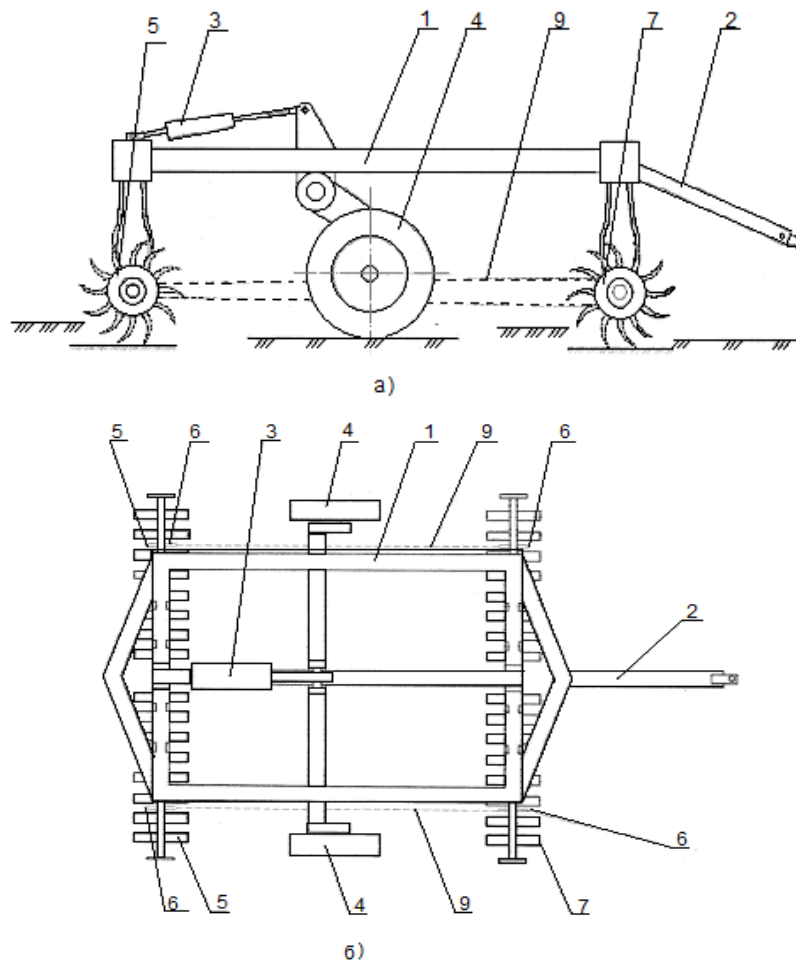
Схема пристрою для обробітку ґрунту: а) вигляд збоку; б) вигляд зверху: 1 – рама; 2 – механізм навіски; 3 – гідроциліндр; 4 – опорні
